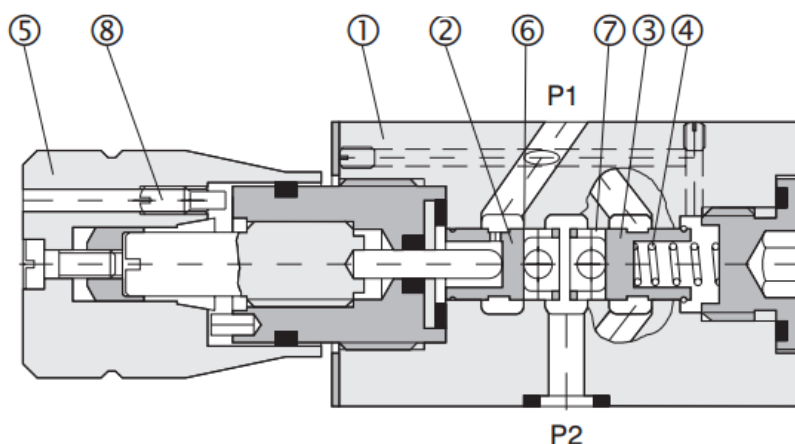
Konstrukční provedení modelu VSS2-206 [3]
